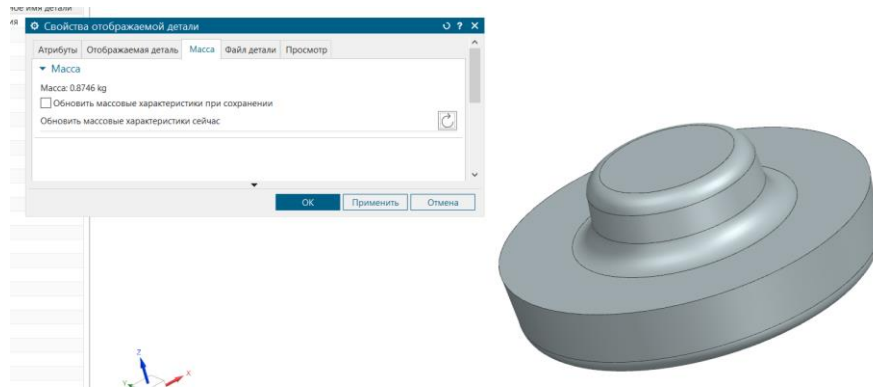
3D-модель заготовки, що отримується на КГШП
